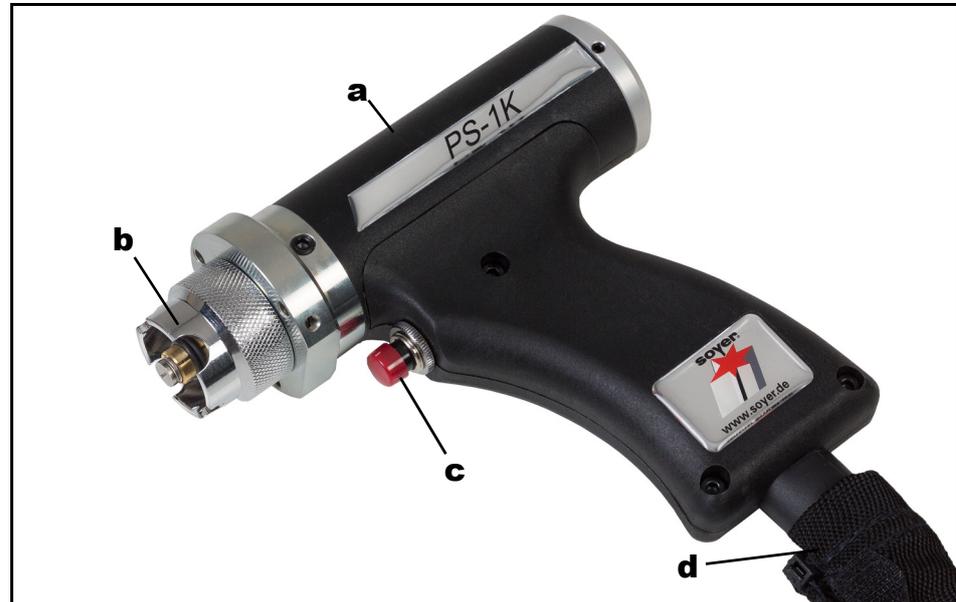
Bolzenschweißpistole PS-1K
